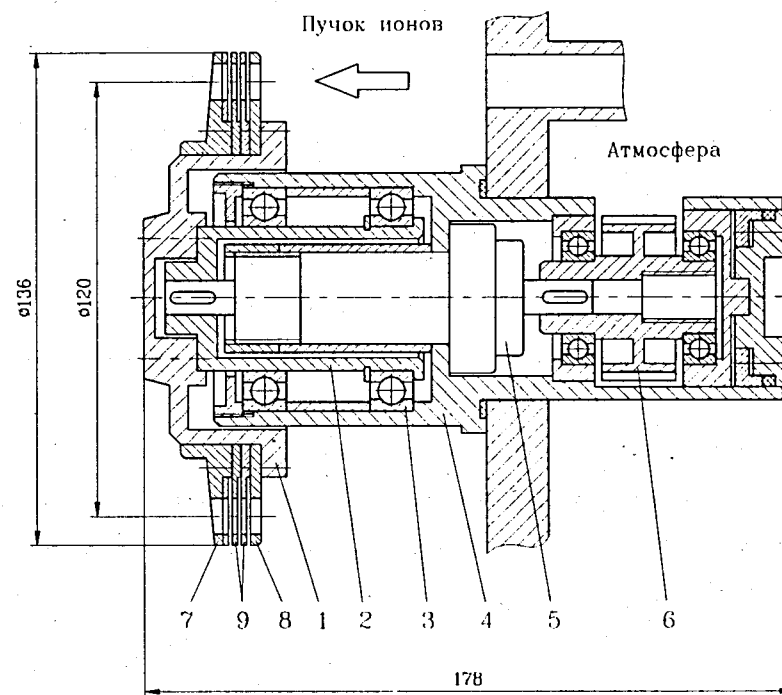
Схема мишенного узла газонаполненного электромагнитного сепаратора продуктов ядерных реакций. 1-ступица; 2-стакан; 3-опорные шарикоподшипники; 4-корпус; 5-магнитожидкостный вакуумноплотный ввод движения; 6-шкив; 7-мишенный диск; 8-диск-маска; 9-диски-поглотители
